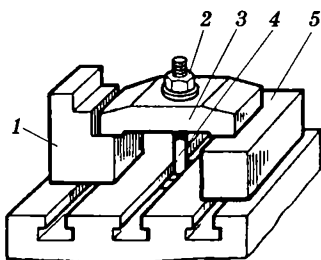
Крепление заготовки прихватами на столе станка:
